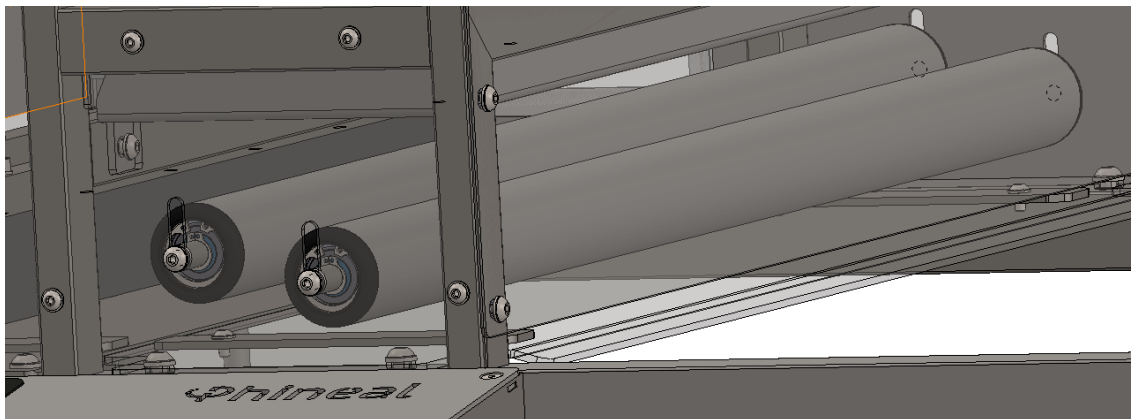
RODILLOS DEL CONJUNTO SUPERIOR
